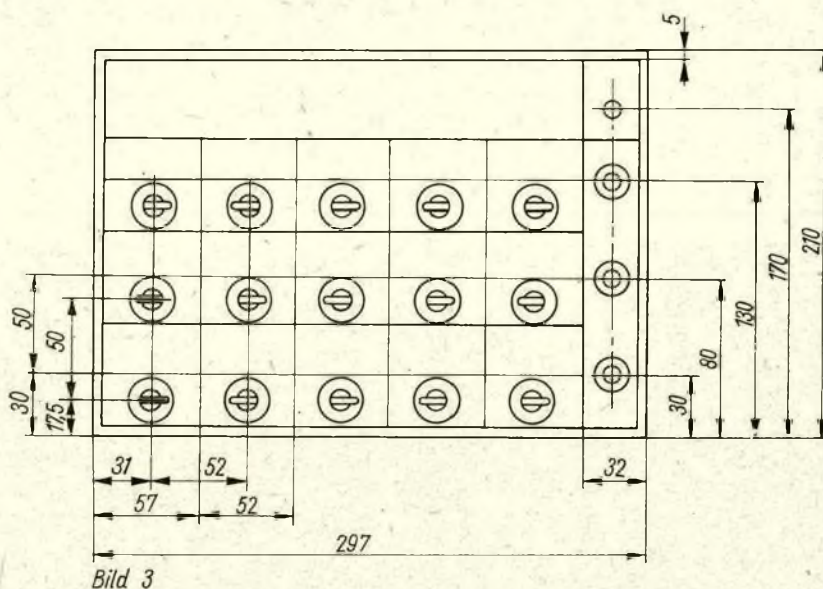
Maßskizze für die Deckplatte der Lernmaschine
